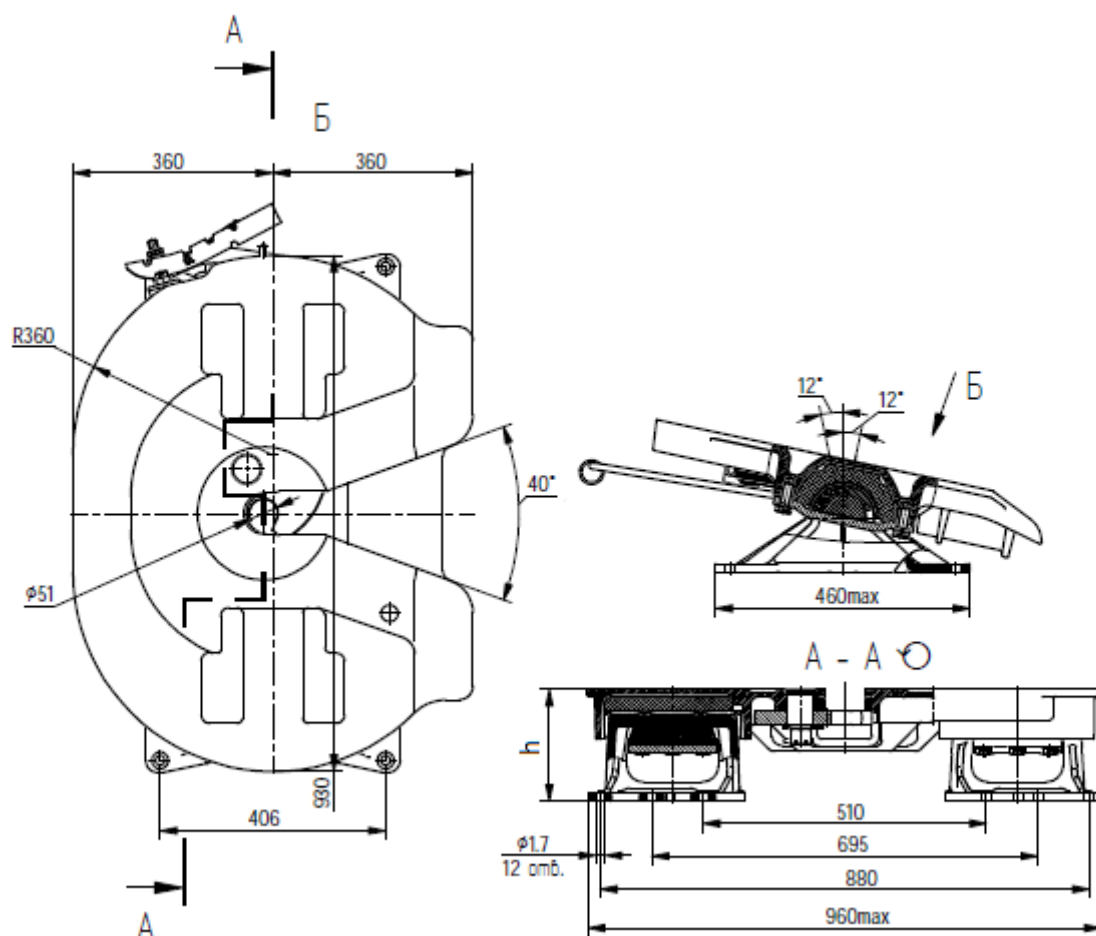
Габаритные и присоединительные размеры седельно-сцепного устройства
